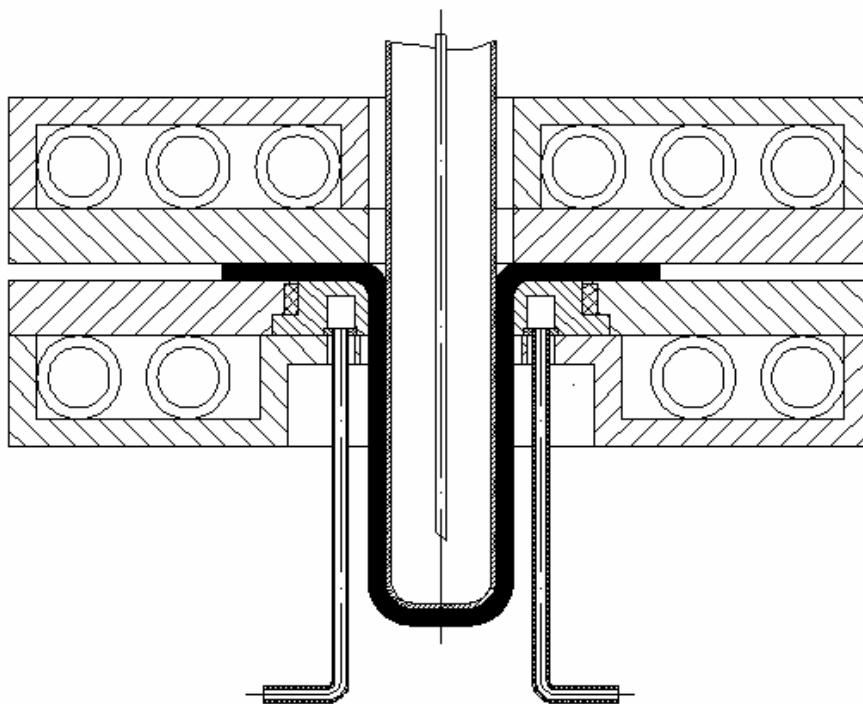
Схема вытяжки с местным подогревом заготовки и охлаждением дна детали
